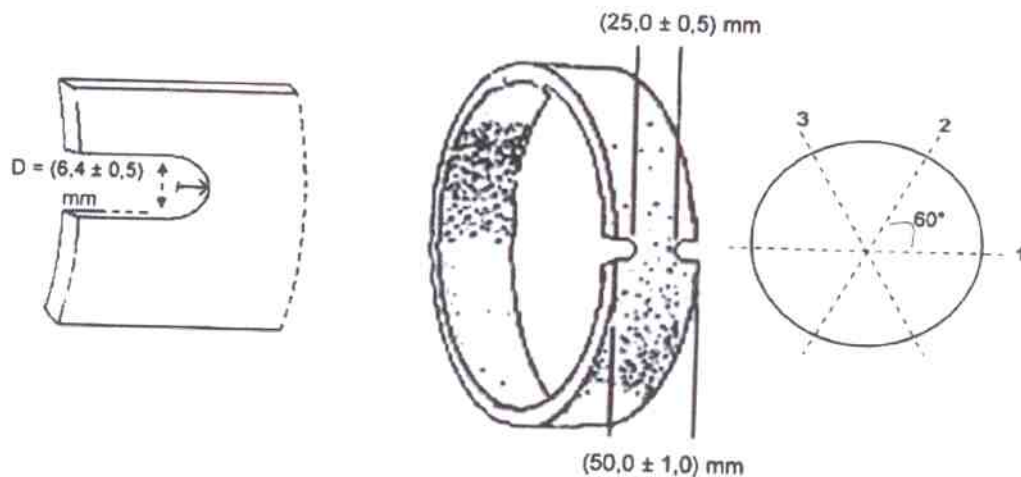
Dimensões do corpo-de-prova com redução de seção
